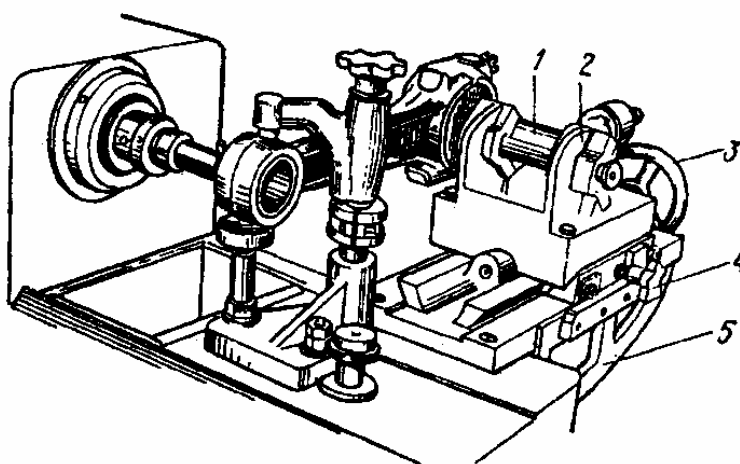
Встановлення шатуна на верстаті УРБ-ВП для розточування верхньої головки та її втулки: 1 – оправка; 2 – призма каретки; 3 – маховик пересувної каретки; 4 – стопорний гвинт; 5 – кронштейн
